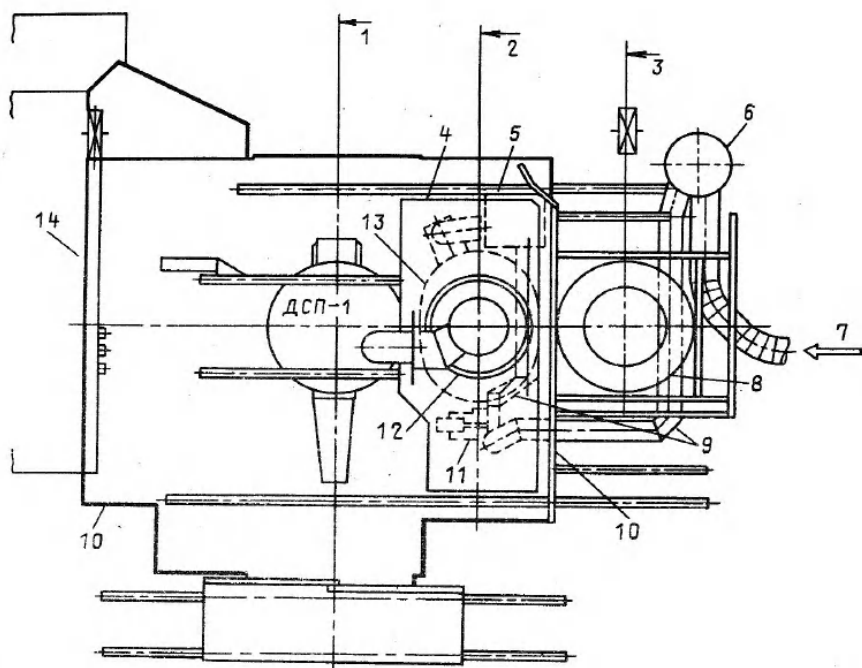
Вид сверху системы дуговая печь – подогреватель лома: 1 – позиция загрузки лома в печь; 2 – позиция нагрева; 3 – позиция загрузки лома в подогреватель; 4 – тележка камеры подогревателя; 5 – охладитель газа; 6 – камера дожигания газа; 7 – от дуговой печи № 2; 8 – желоб для лома; 9 – газовый канал; 10 – камера-укрытие; 11 – вентилятор-дымосос; 12 – камера подогревателя; 13 – нижняя крышка; 14 – камера трансформатора
